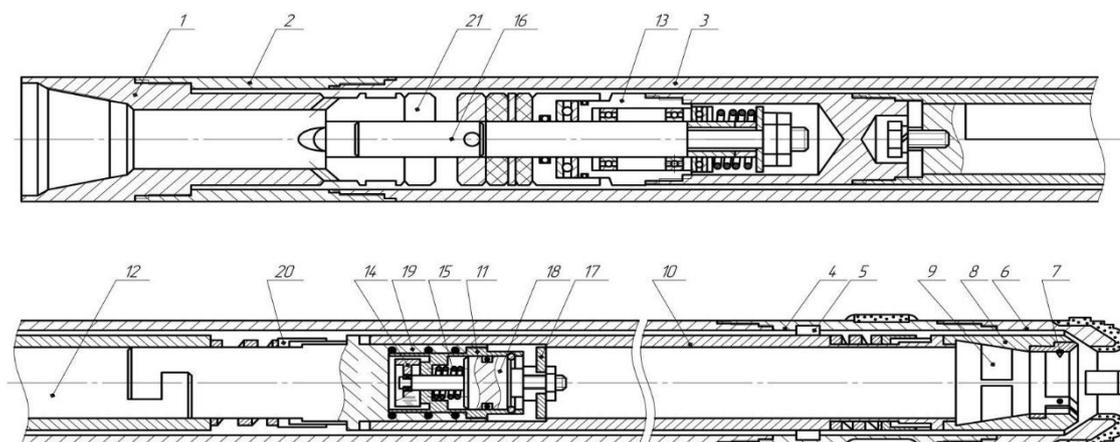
Общий вид керноориентатора АКО-59: 1 – переходник, 2 – центратор, 3 – труба колонковая, 4 – расширитель, 5 – стабилизатор; 6 – коронка, 7 – керноотметчик, 8 – корпус кернорвателя, 9 – кольцо рвательное, 10 – труба керноприемная, 11 – датчик контрольный, 12 – груз-отвес, 13- узел подшипниковый, 14 – отвес, 15 – пружина, 16 – шпindelь, 17 – шайба, 18 – поршень, 19 – окно смотровое, 20 – кольцо фиксирующее, 21 – контргайка.
